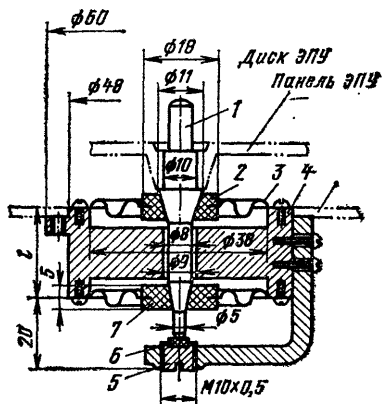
Виброзащитная конструкция вала диска ЭПУ.
